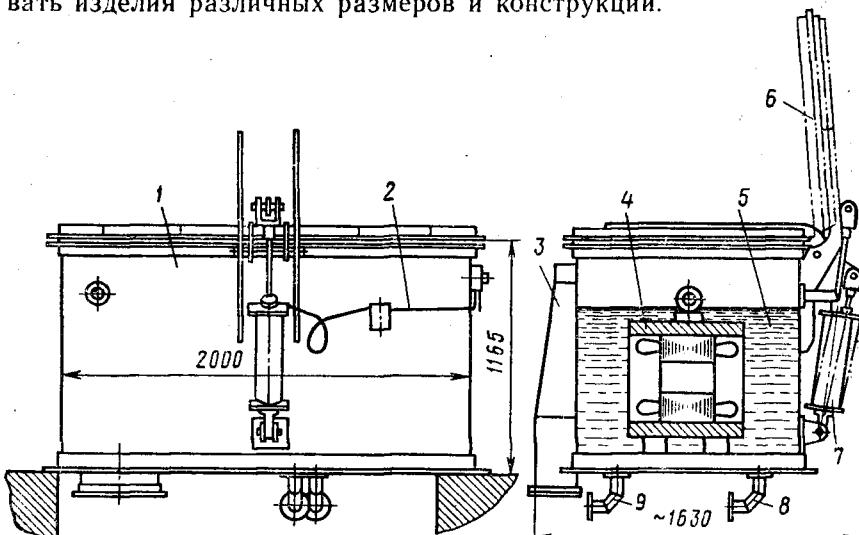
Пропиточная ванна с пневматическим приводом для открывания и закрывания крышки:
